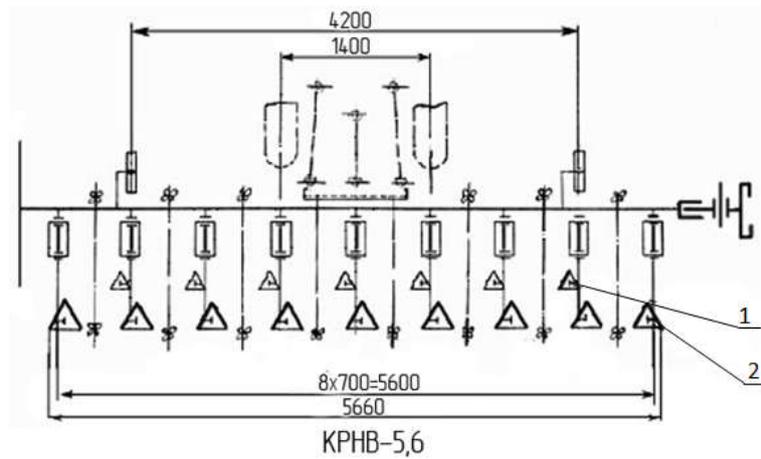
Схема розташування робочих органів для міжрядь 70 см:
